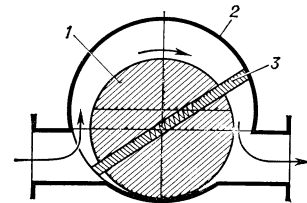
Схема шибберного пластинчатого насоса: 1 — ротор; 2 — корпус; 3 — пластина (шиббер).
